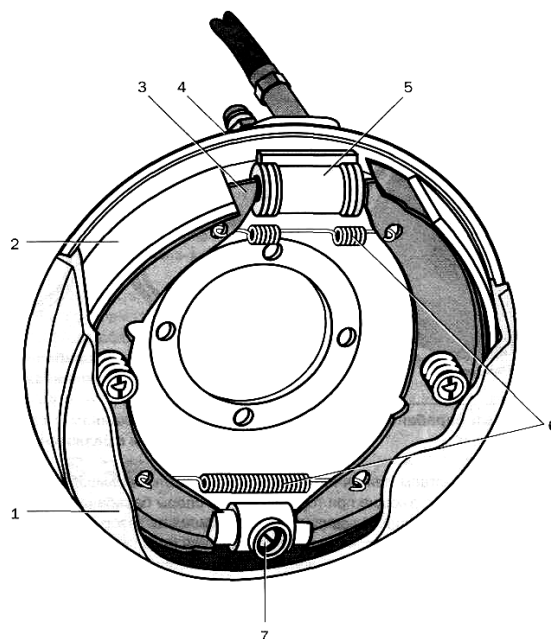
Барабанный механизм с равными приводными силами и односторонним расположением опор колодок:
